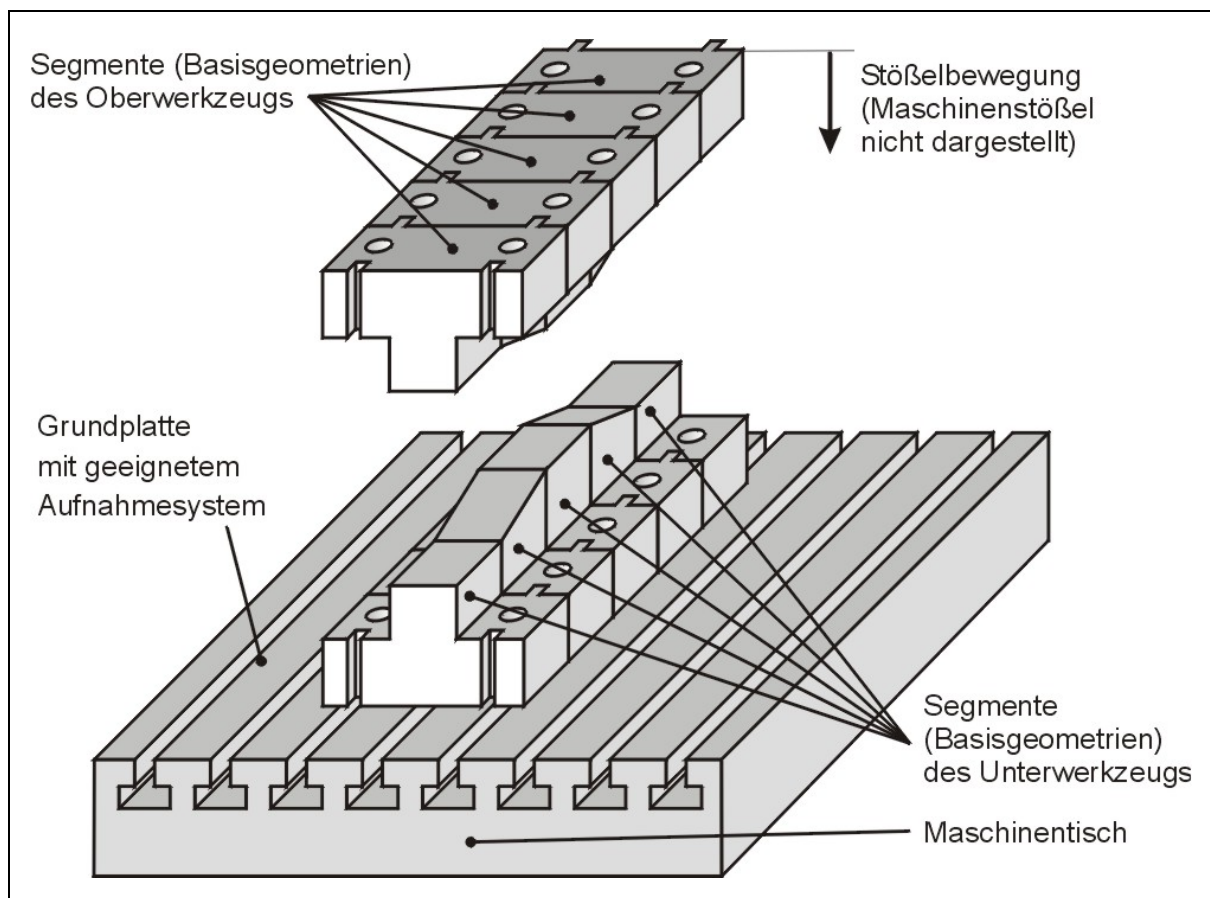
Werkzeugprinzip zum Präzisionsschmieden hinterschnittener Gleichlaufgelenke (3. Umformstufe) [WIE96]
